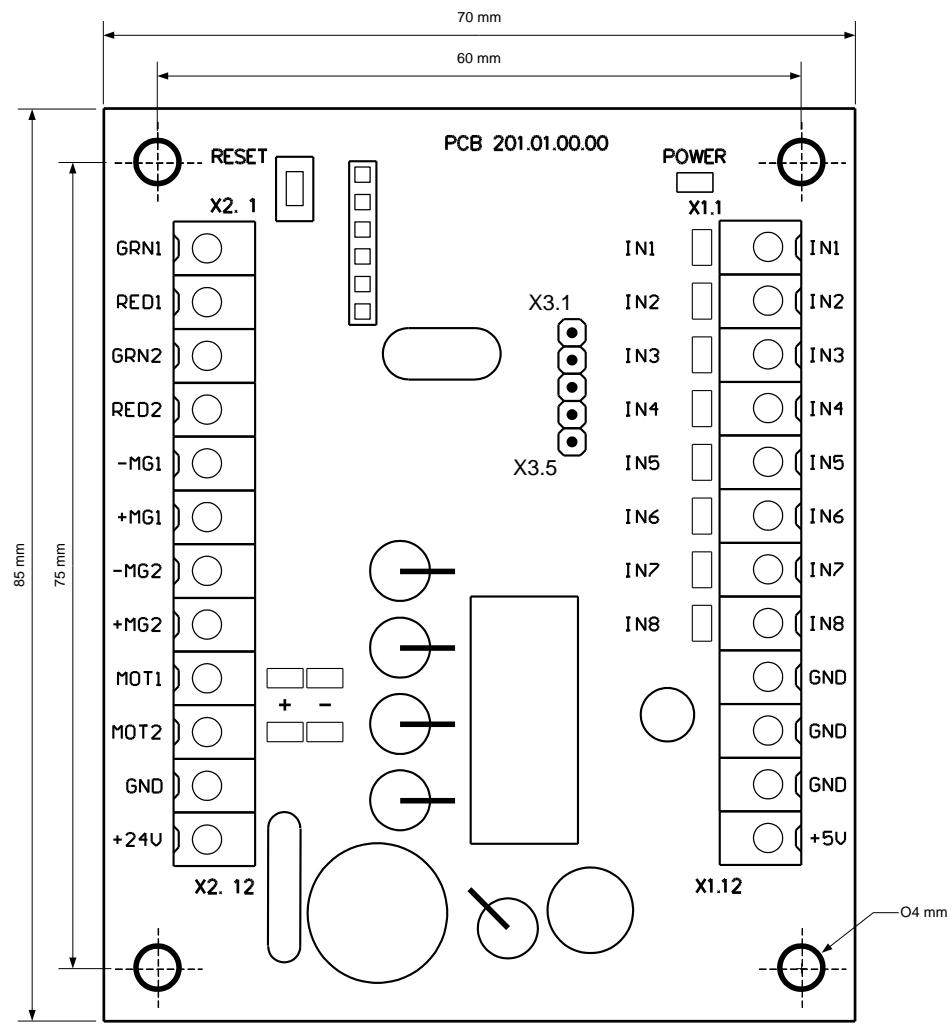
Внешний вид контроллера PCB.201.01.00.00
